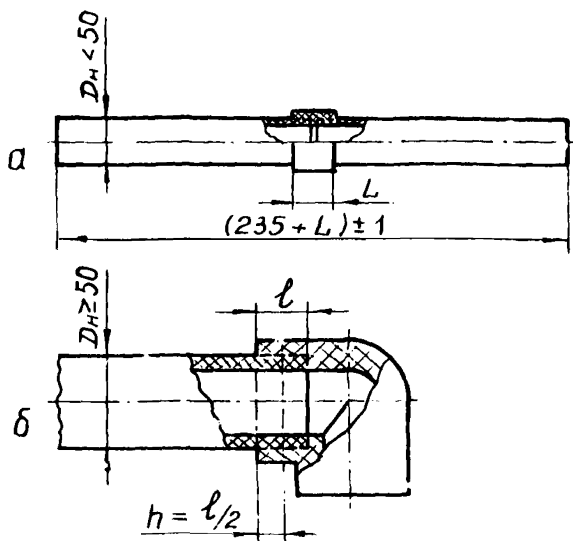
Образцы для испытаний сварных раструбных соединений:
